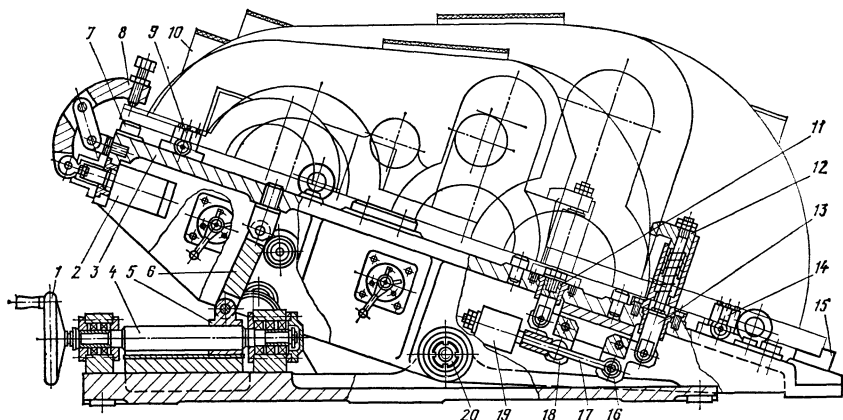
Специализированное безналадочное приспособление для фрезерования плоскостей корпусов (крышек) редукторов
